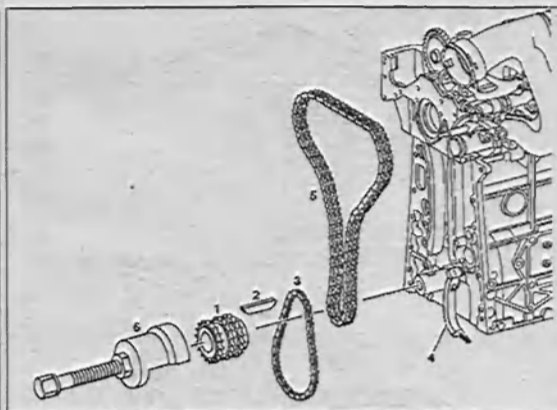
Снятие и установка зубчатого шкива коленчатого вала:
